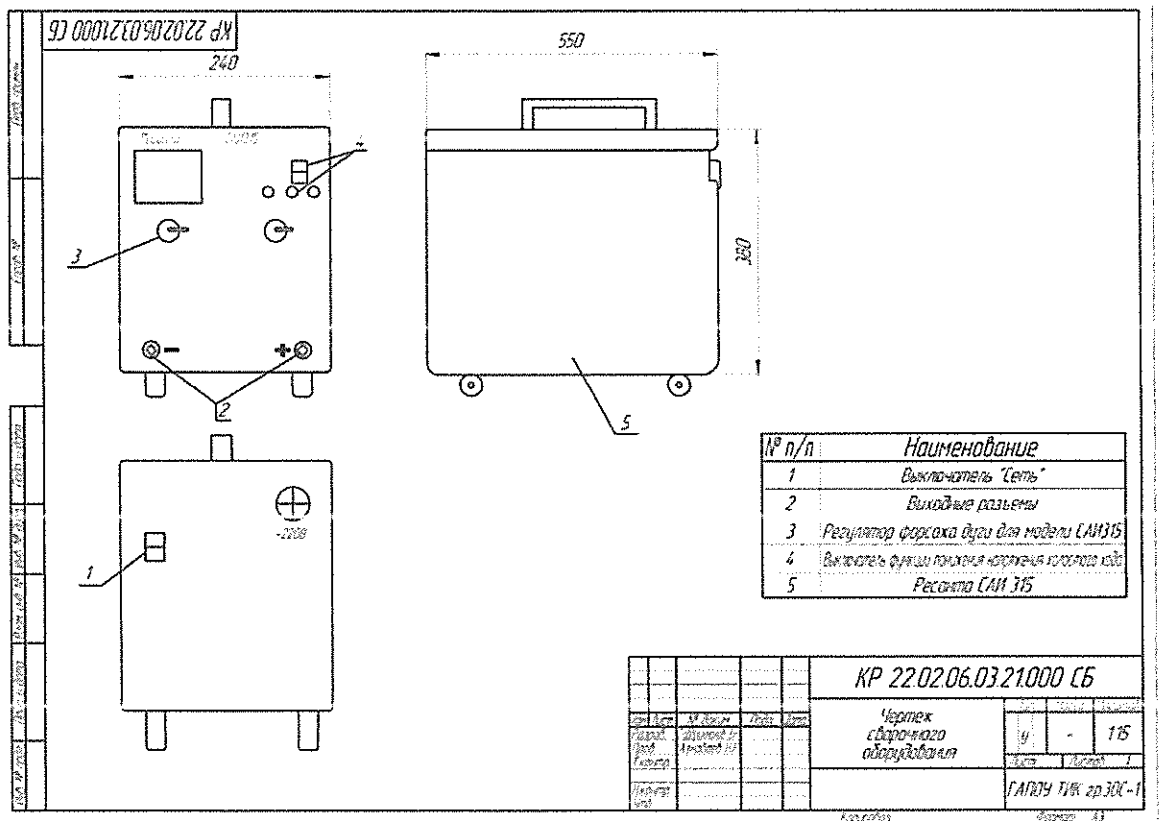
Образец чертежа сварочного оборудования
